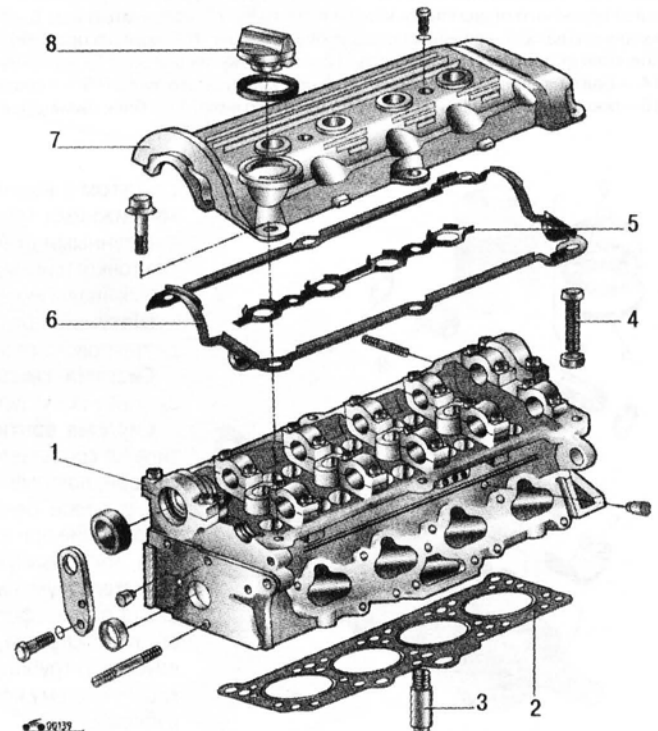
Головка блока цилиндров двигателей DOHC: 1 - головка блока цилиндров; 2 - прокладка головки блока цилиндров; 3 - направляющая втулка клапана; 4 - болт; 5, 6 - прокладки крышки головки блока цилиндров; 7 - крышка головки блока цилиндров; 8 - пробка маслоналивной горловины
